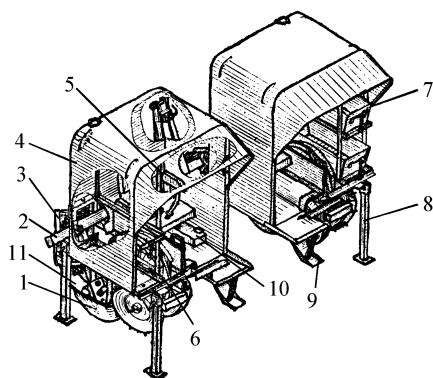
Лесная сажалка СЛП-2: 1 – сошник; 2 – брус навески; 3 – рама; 4 – кабина; 5 – сидение сажальщиков; 6 – посадочный аппарат; 7 – ящик для сеянцев; 8 – стойка-подставка; 9 – подножка; 10 – ящик для инструмента; 11 – опорный башмак
